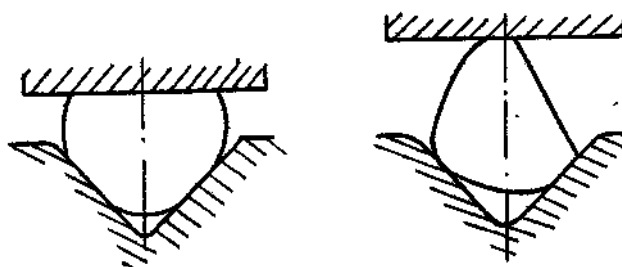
Схема кантовки образца при протяжке в комбинированных бойках.
